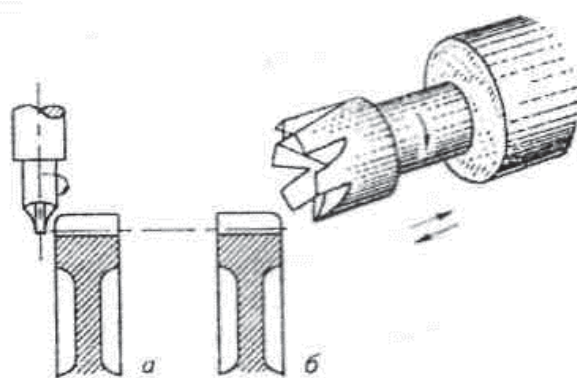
Схемы закругления зубьев цилиндрических зубчатых колес:
